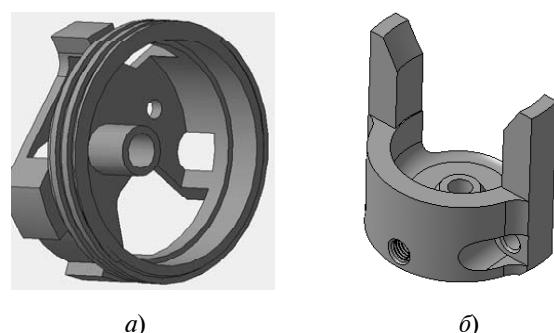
Корпусные миниатюрные детали маложёсткого корпуса (а) и повышенной мягкости (б)
